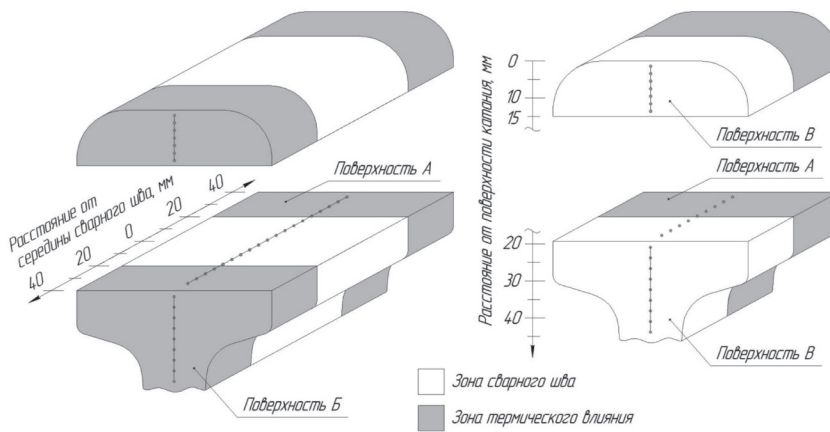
Схема расположения поверхностей и мест нанесения отпечатков при измерении твердости головки рельса алюминотермитного сварного соединения
